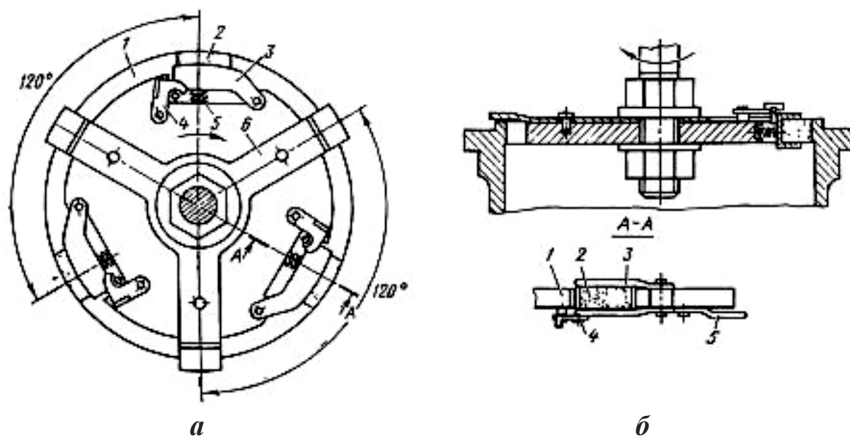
Пристрій для зняття напрацювання у втулках:
